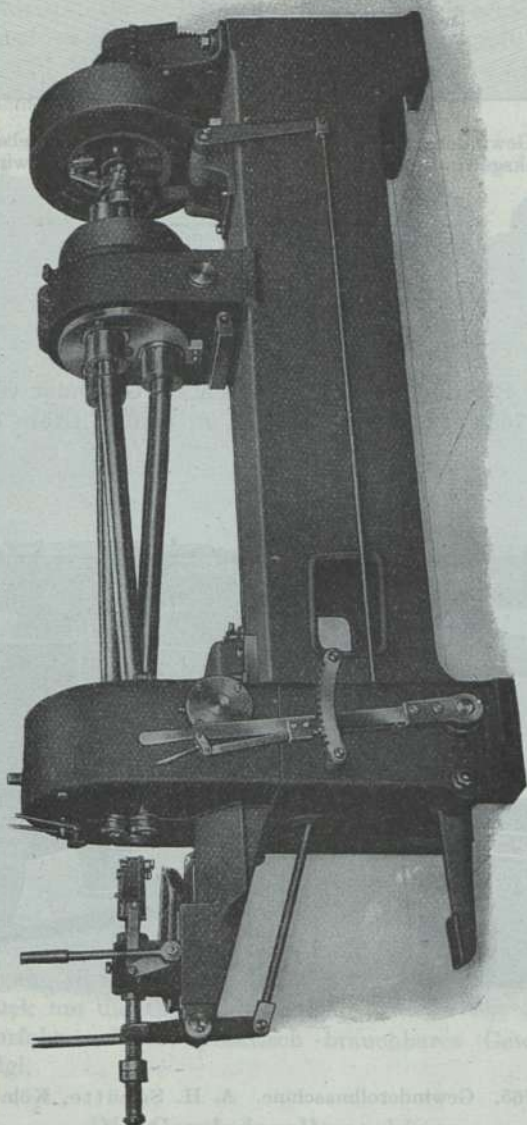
Gewindewalzmachine. A. H. Schütte, Köln-Deutz.
